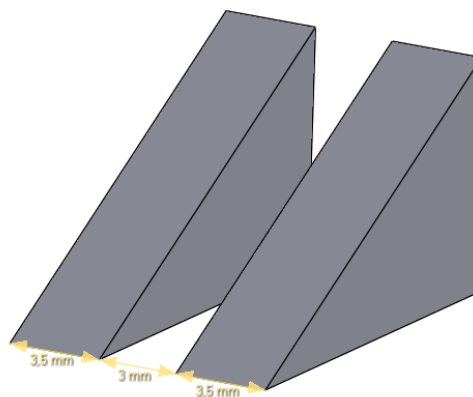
Imagen del CAD del segundo tipo de soporte diseñado para la fabricación de la pieza 8 en la que se pueden apreciar las dimensiones de cada una de las partes y de la separación entre ellas.
